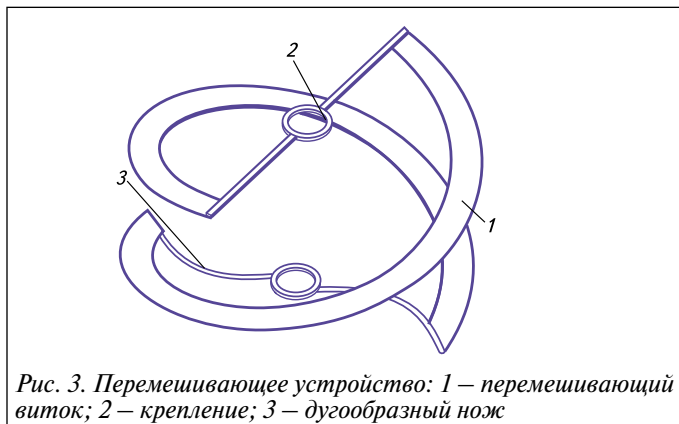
Перемешивающее устройство: 1 – перемешивающий виток; 2 – крепление; 3 – дугообразный нож
